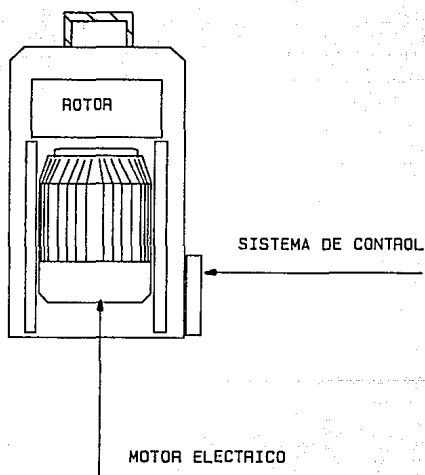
CUBIERTA CILINDRICA MOVIL PARA MOTOR Y ROTOR
